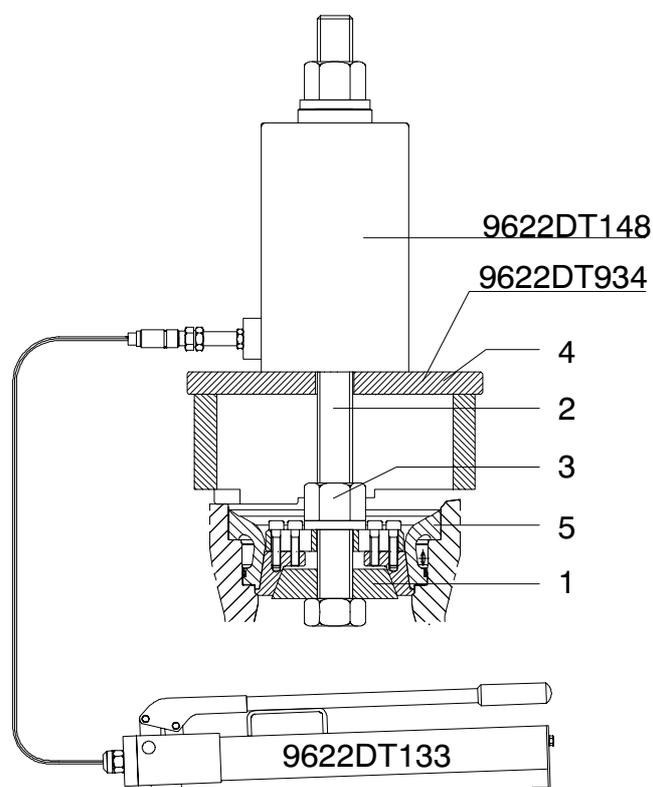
15 Desmontaje de asientos de válvula
